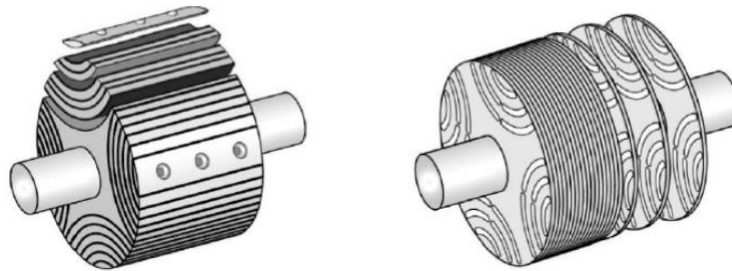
Rotor laminado axialmente (à esquerda); Rotor laminado transversalmente (à direita) [15,19].
